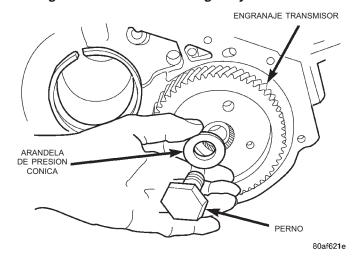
Instalación de perno y arandela del engranaje transmisor
